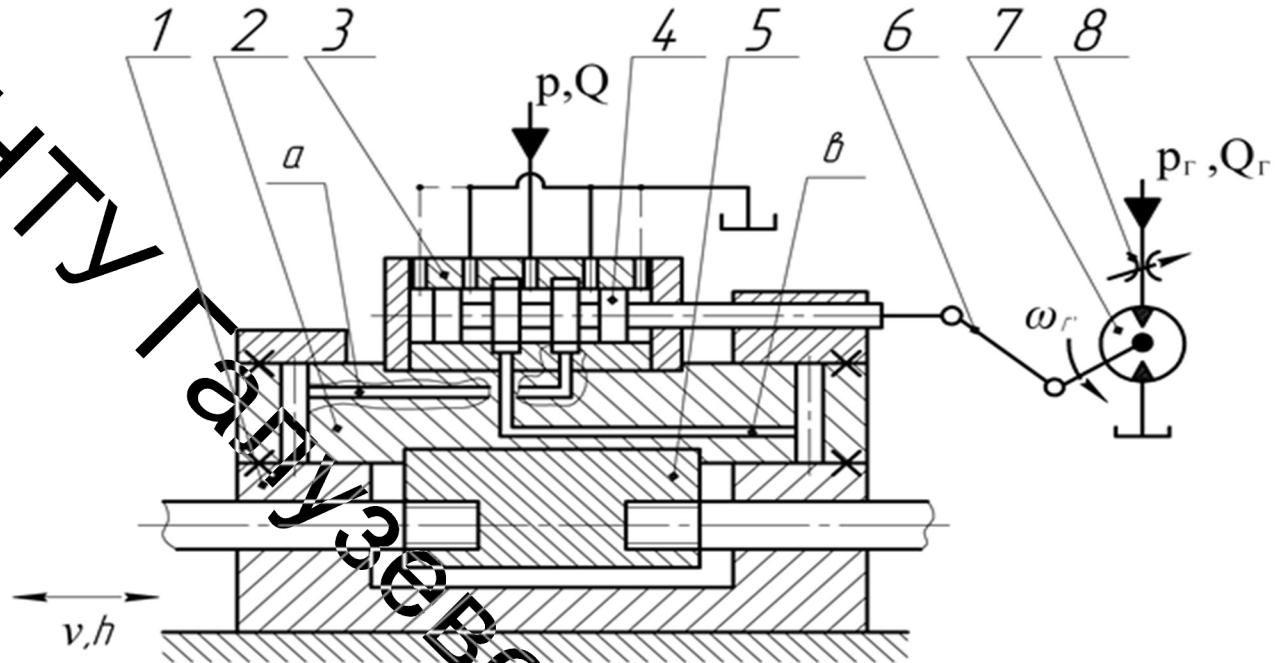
Конструктивна схема привода вібросупорта *ВГ-2
